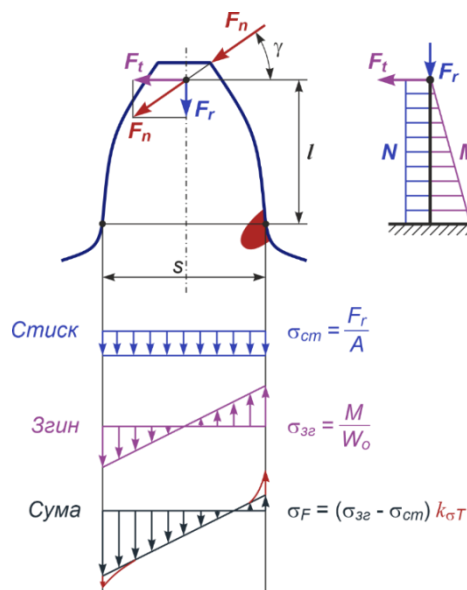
Схема розрахунку зуба зубчастого колеса на згин.
